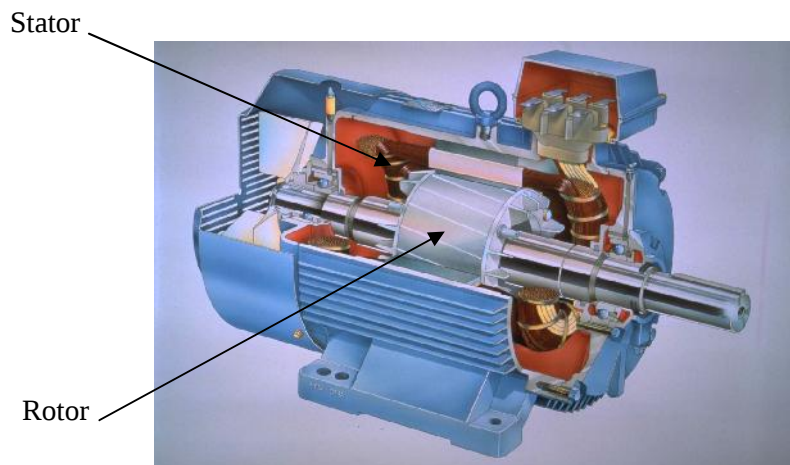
Structure de la machine asynchrone triphasée à cage.
